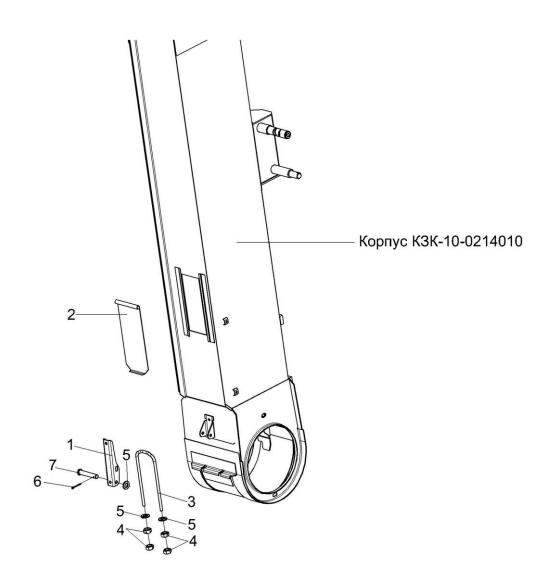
Элеватор зерновой КЗК-10-0214000 (лист 4)
